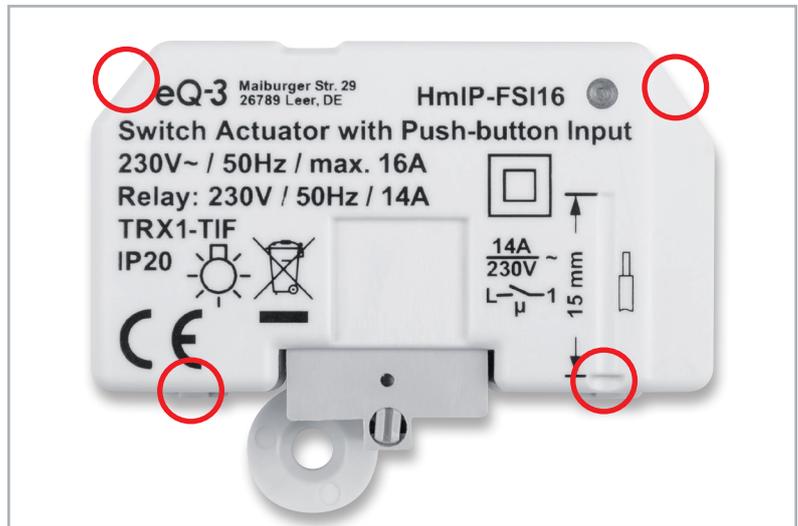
Beim Zusammenstecken der Gehäuseteile ist das Einrasten der vier Befestigungsclips zu prüfen.
